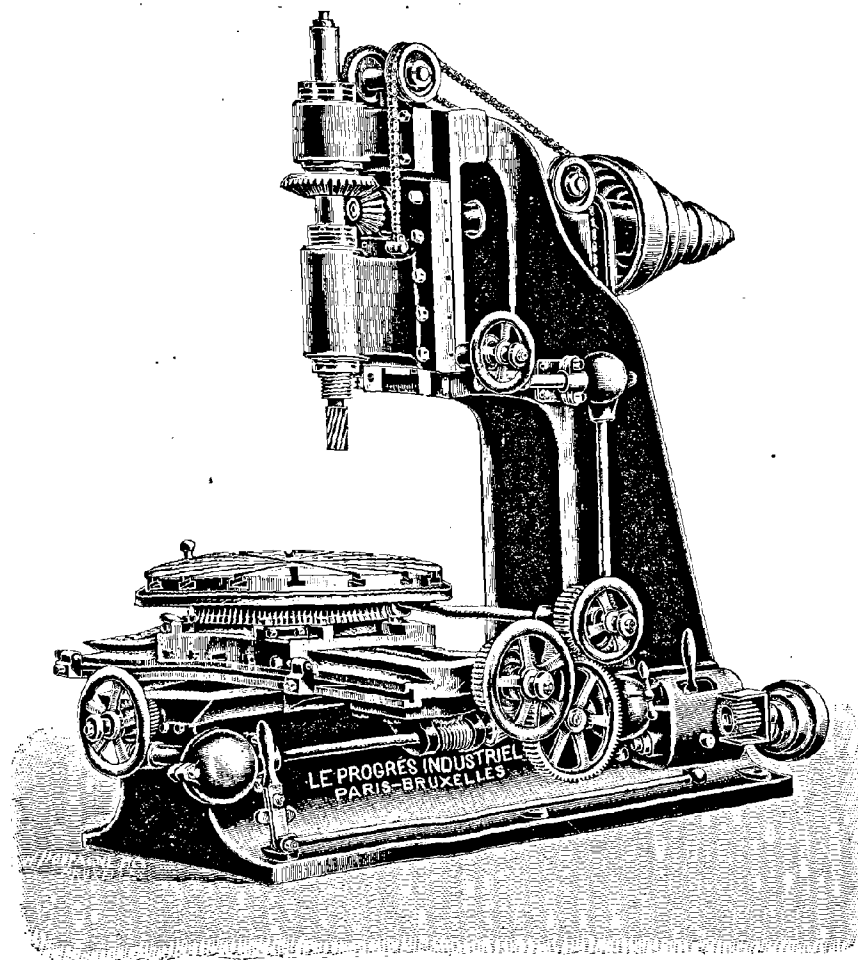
Machine à fraiser verticale automatique du Progrès Industriel.
